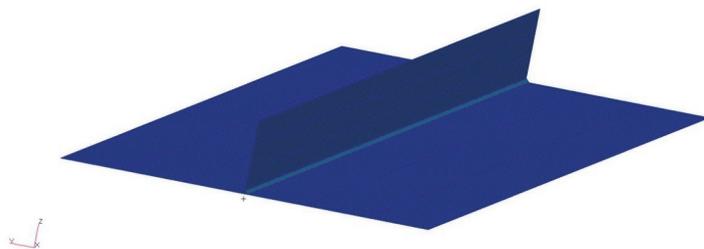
Конечно-элементная модель конструкции со сварочными присадками
